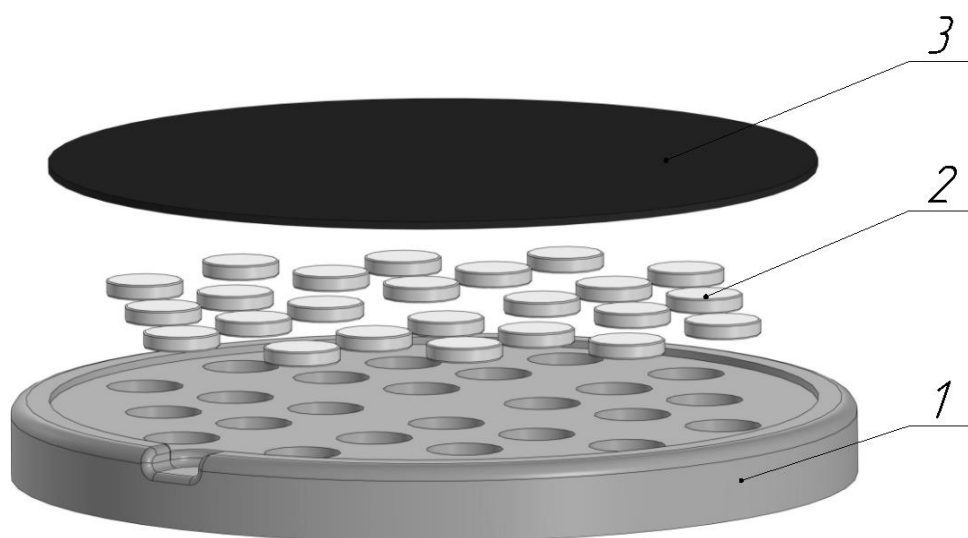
Взрыв-схема основания: корпус, магниты, металлическая пластина
